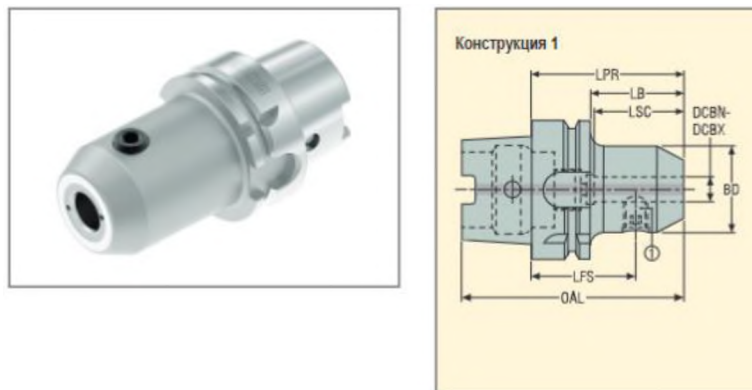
Weldon DIN 1835 (HСКА63-ЕМО8-065-Л1) з конусом шпинделя HSK-A63 [6 с.78]
